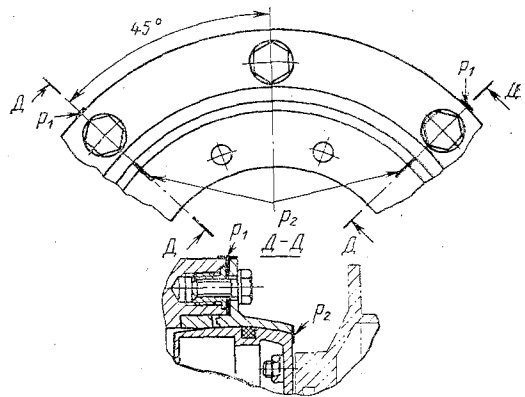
Расположение установочных рисок  $p_1$  и  $p_2$  на фланцах сферической втулки и крышки
